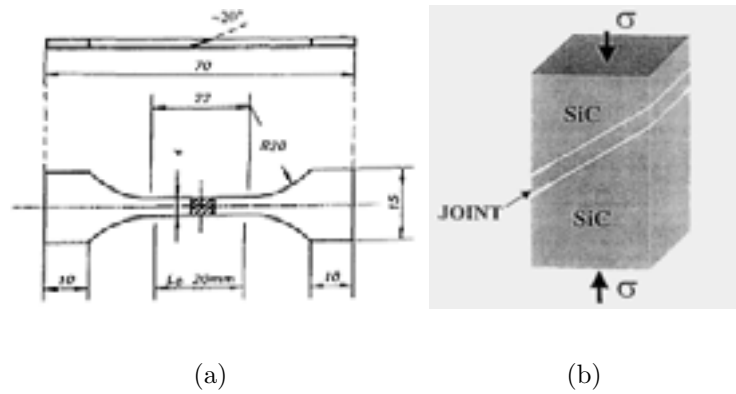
Essais sur éprouvettes avec joint incliné : traction [75] (a) et compression [76] (b)
